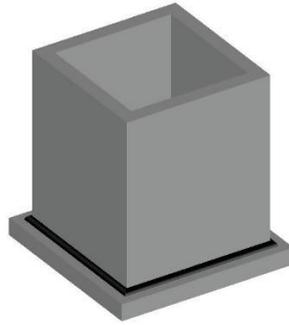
Сварное соединение стойки с основанием.
